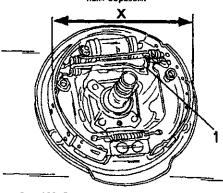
Для выставки диаметра тормозных колодок поворачивать установочное колесо.
